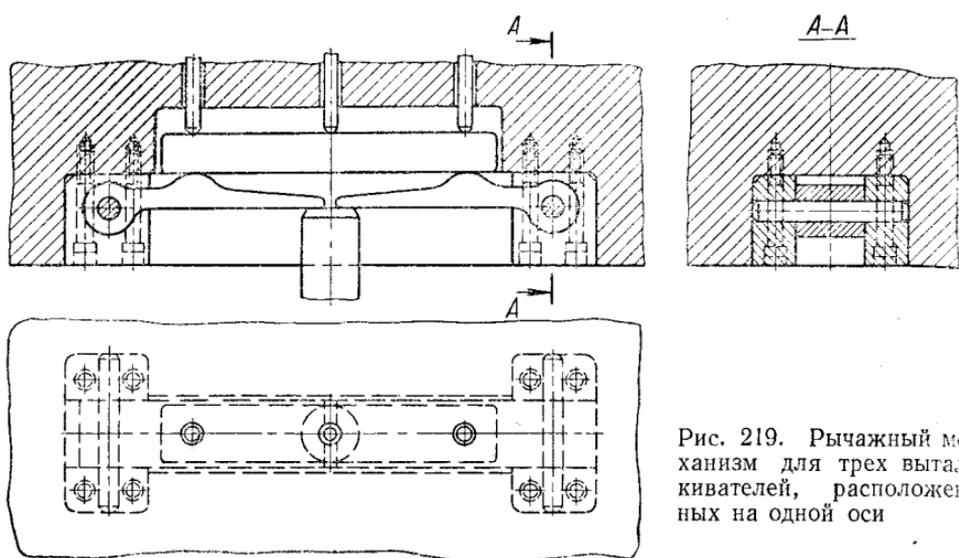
Рычажный механизм для трех выталкивателей, расположенных на одной оси
